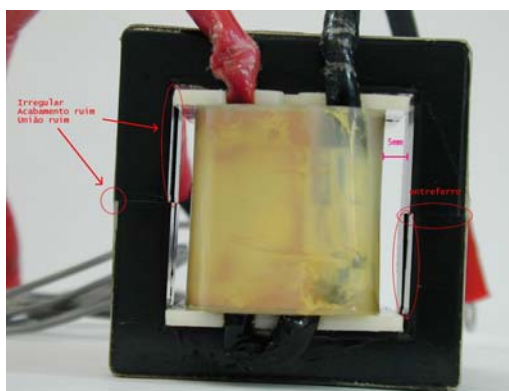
Vista frontal do transformador de alta frequência utilizado pela fonte de soldagem.
